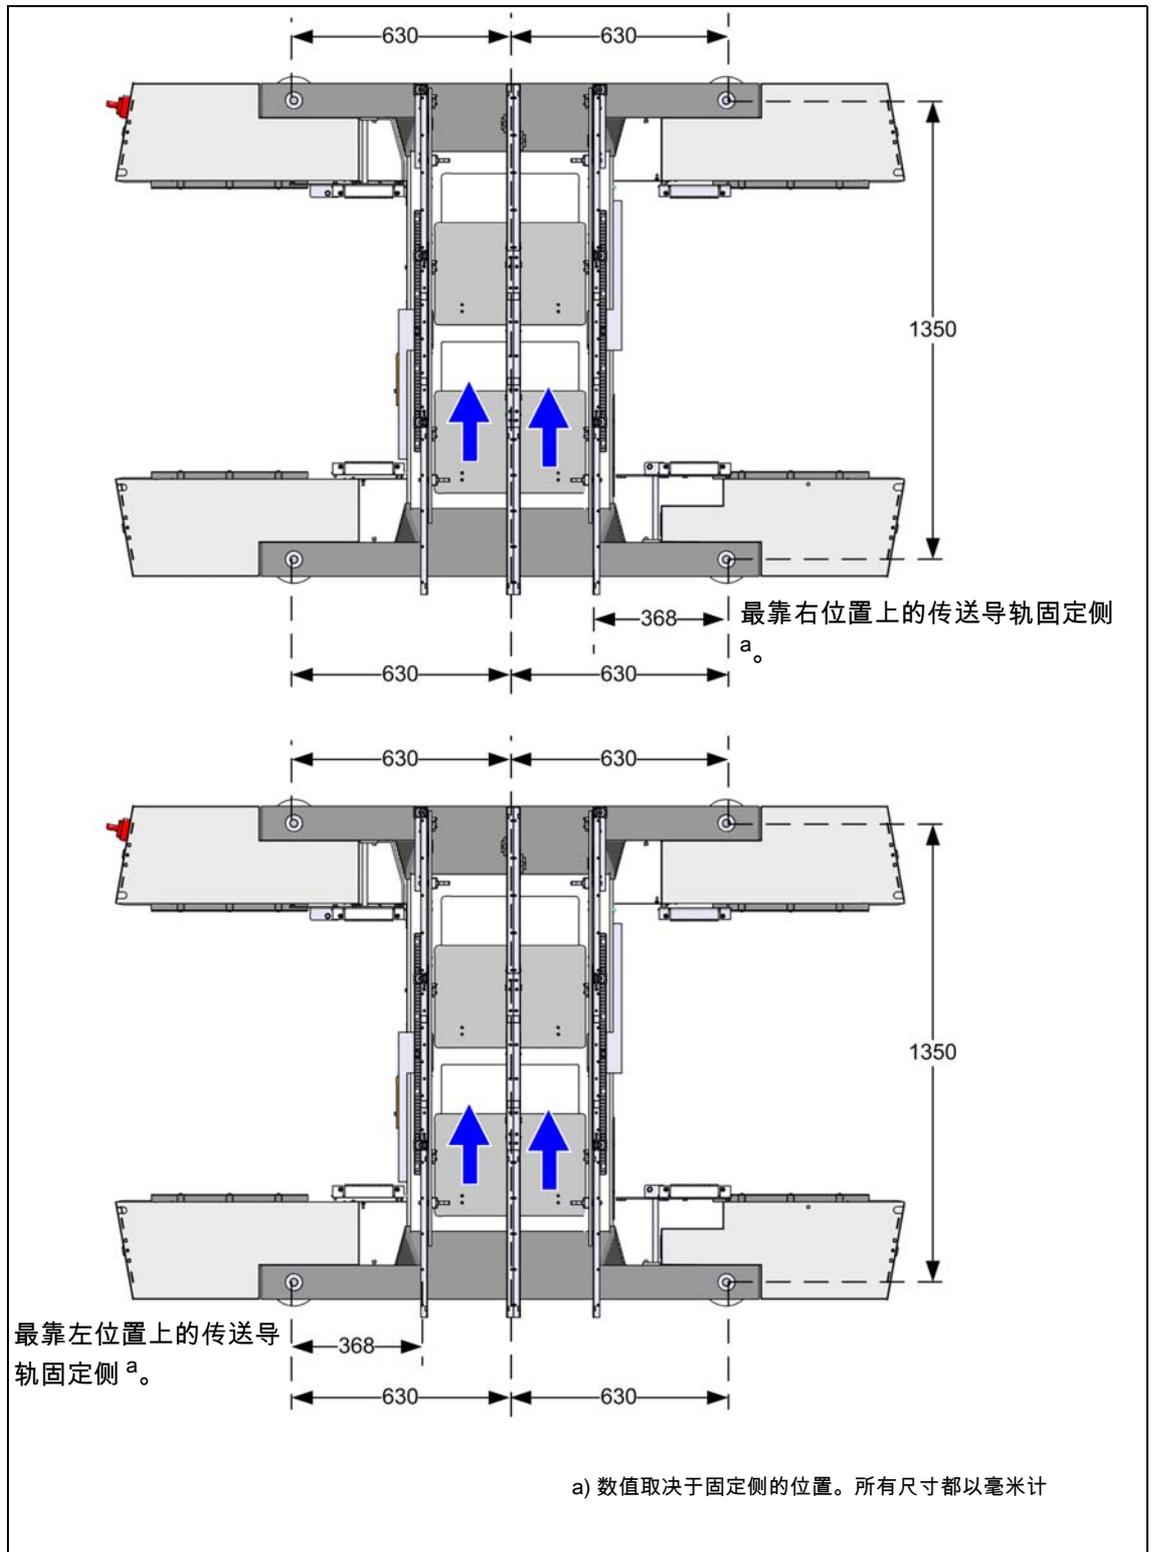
PCB 双传送导轨的贴片机支脚间隙 (以毫米为单位)
